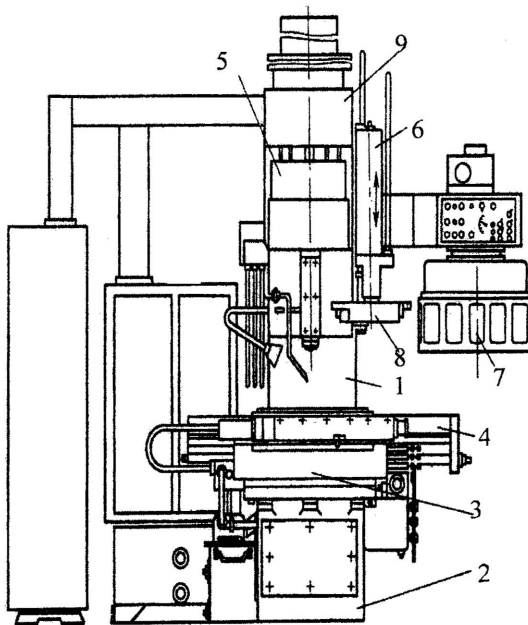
Общий вид вертикально-фрезерного станка мод. ЛФ-260МФЗ с ЧПУ станка
